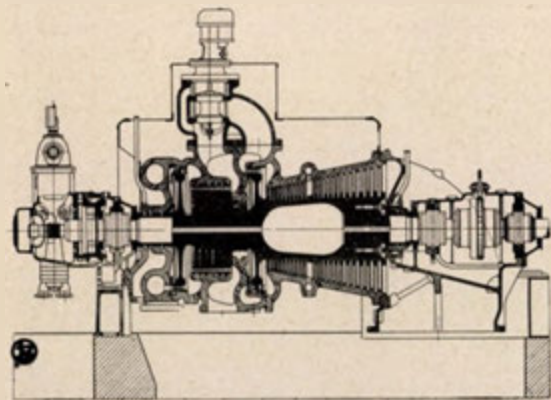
P. B. Rotor parní turbíny 24.000 kW, 3000 o./m.
